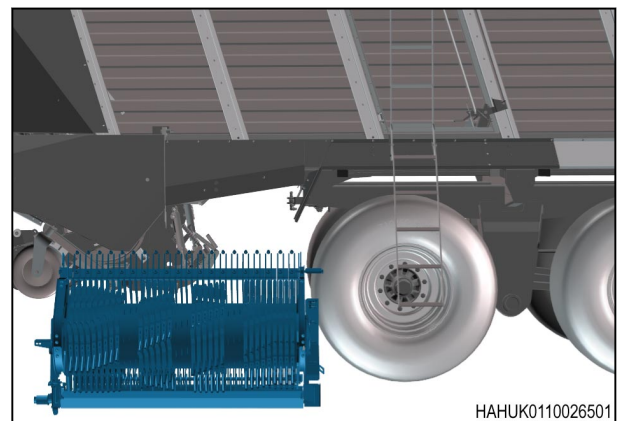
Bewegen Sie die Messerbaugruppe auf die Seite der Maschine
